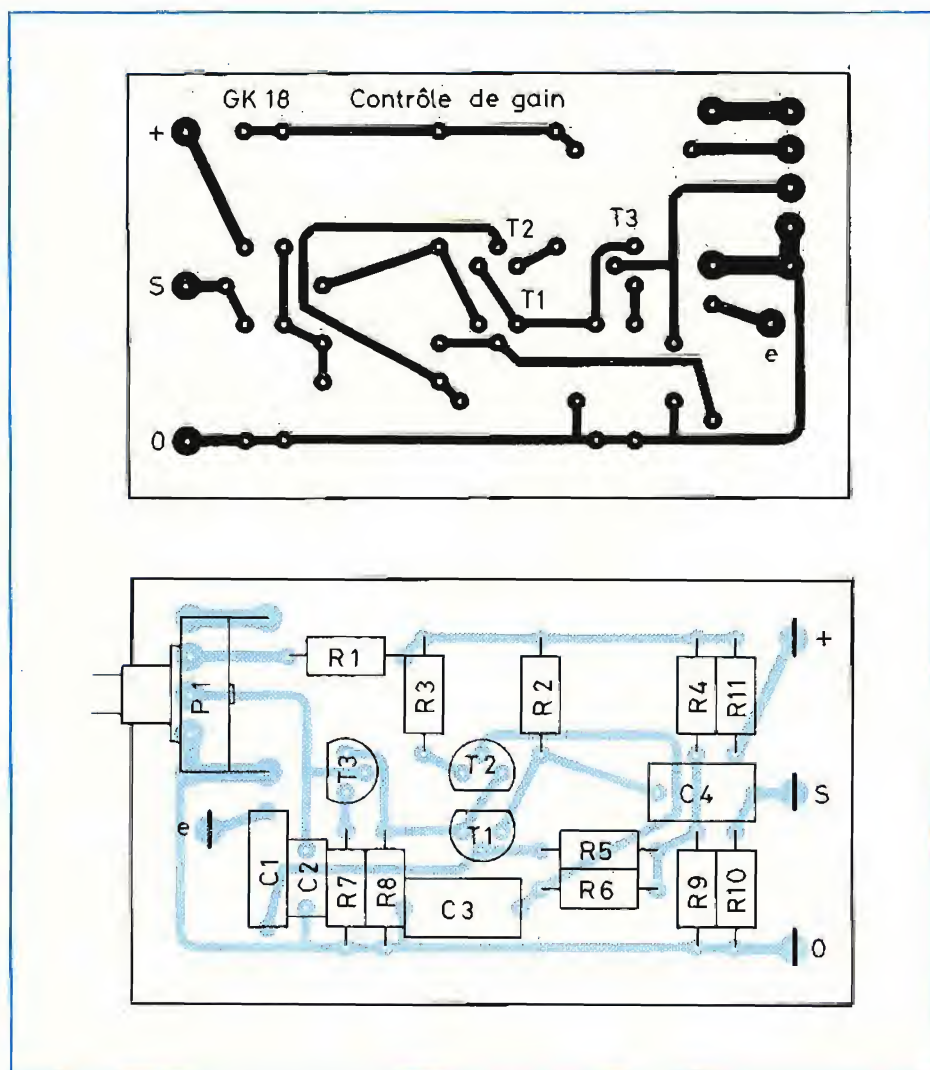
In alto (A) lato rame del circuito stampato su cui può essere montato il dispositivo di controllo automatico del guadagno, ed in basso (B) il lato dei componenti.
